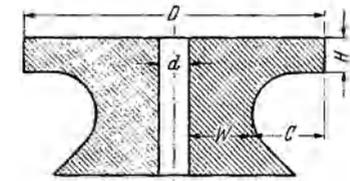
Hauptmasse für hinterdrehte Fräser.
